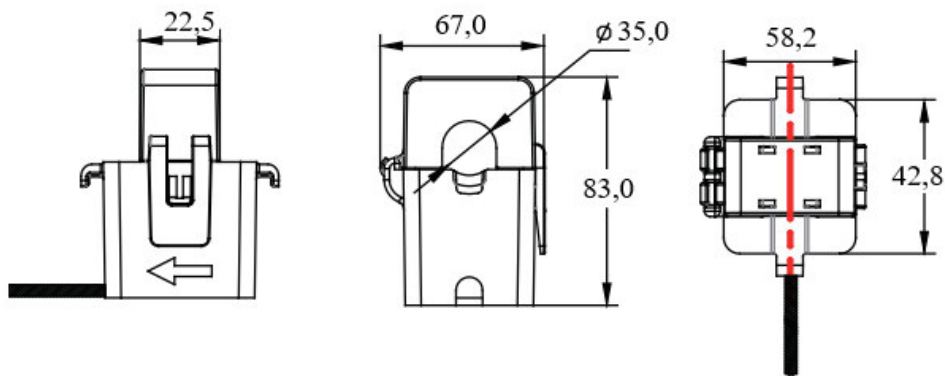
Внешний вид и габаритные размеры датчика SCT400
